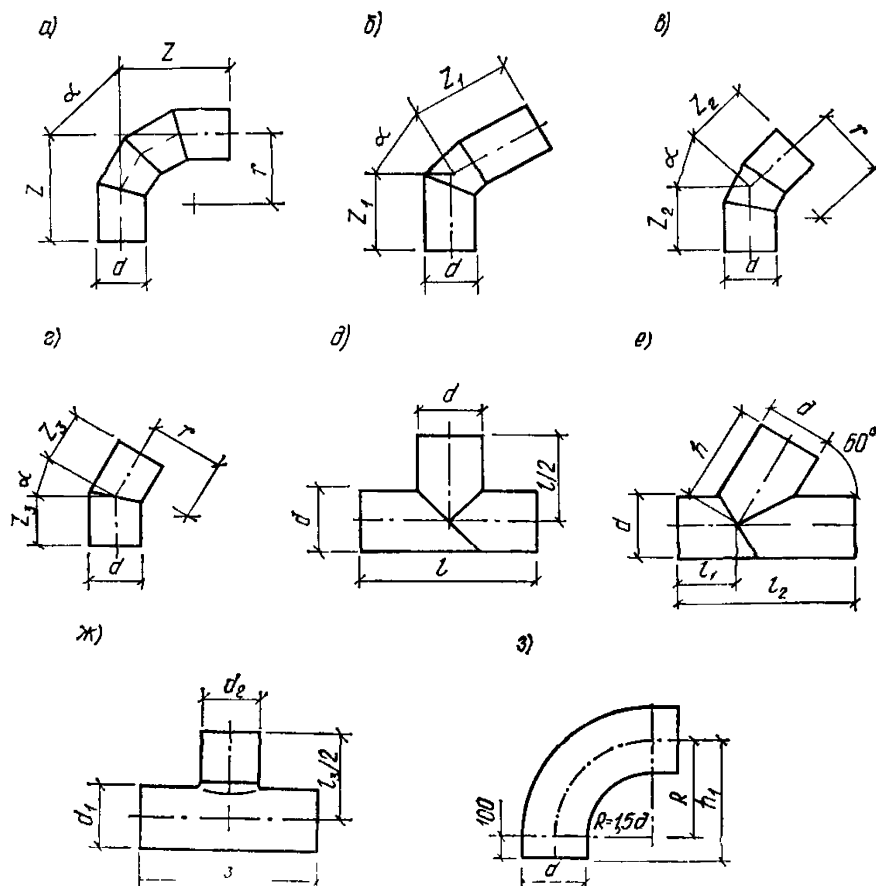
Соединительные детали из ПНД, получаемые из отрезков труб: а — отвод сварной 90°; б — отвод сварной 60°; в — отвод сварной 45°; г — отвод сварной 30°; д — тройник сварной; е — тройник сварной 60°; ж — тройник сварной неравнопроходный; з — отвод гнутый
